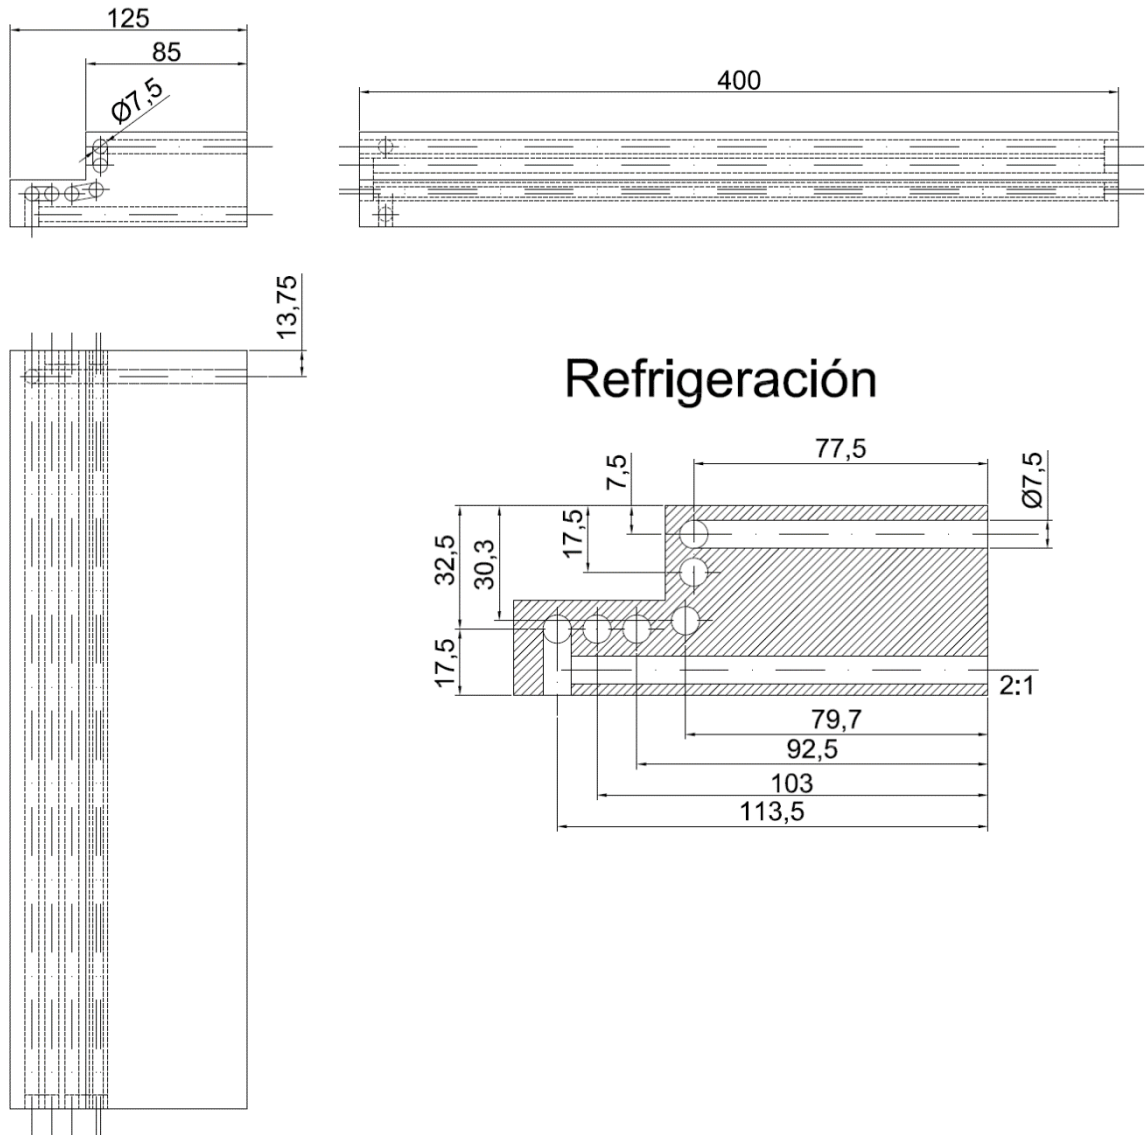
Diseño ITMA en detalle del Molde de Cobre aplicable a heat inputs hasta 3kJ/mm. Detalle de mordaza 2.
